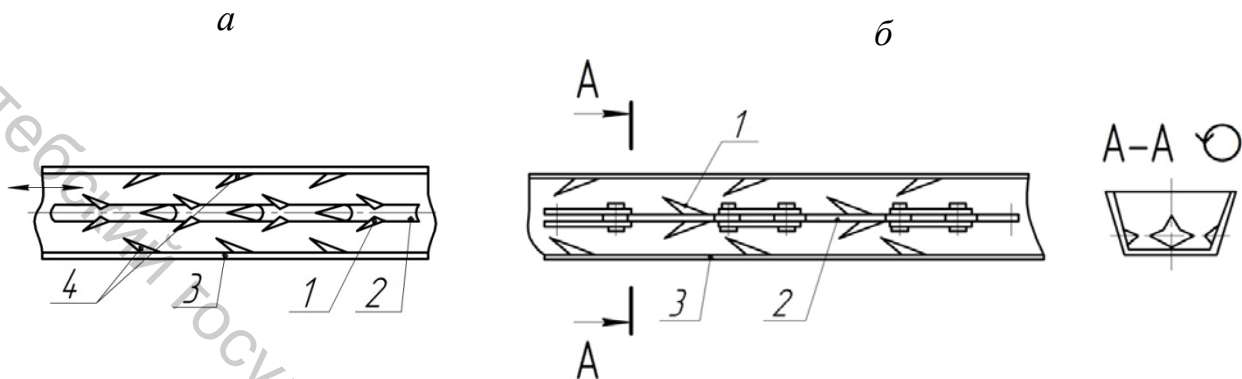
Ершово-штанговый (а) и цепной (б) конвейеры для удаления стружки
